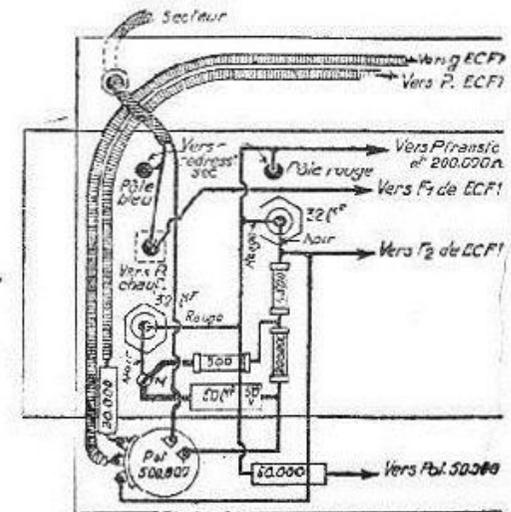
Plan complémentaire pour Minime secteur sans valve CY 2. Ce plan remplace la partie correspondante du plan, fig. 46.
